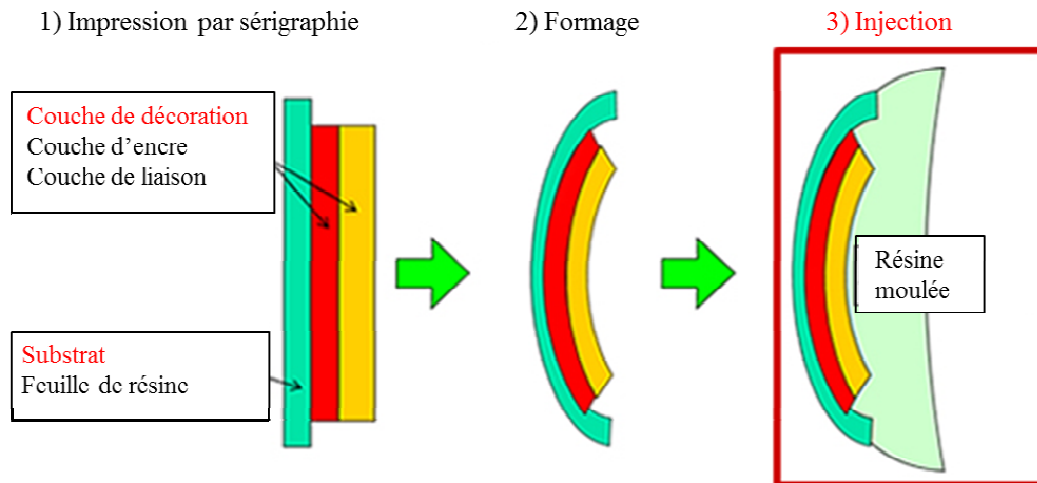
Schéma du procédé d'IML (In Mould Labeling)
